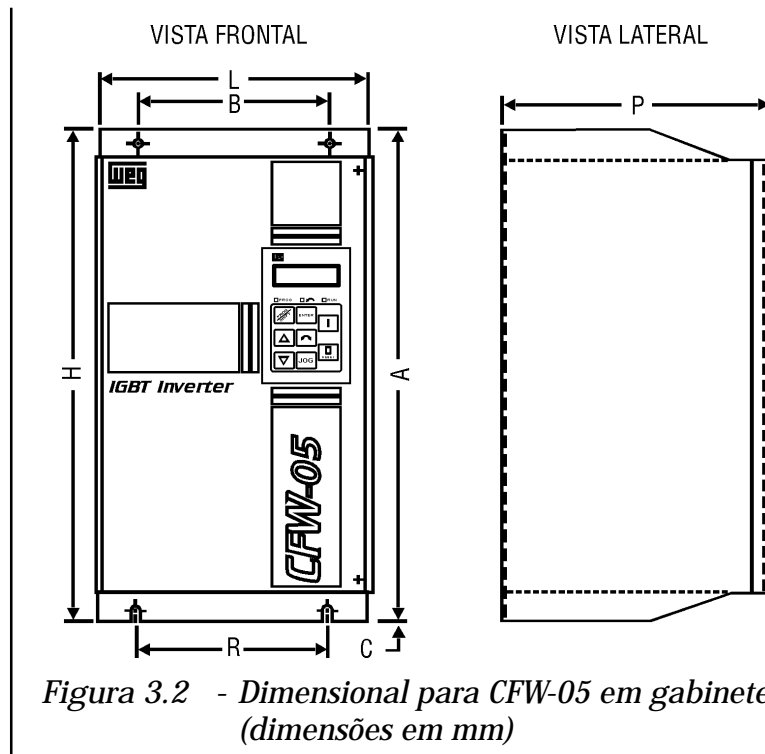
Dimensional para CFW-05 em gabinete (dimensões em mm)
